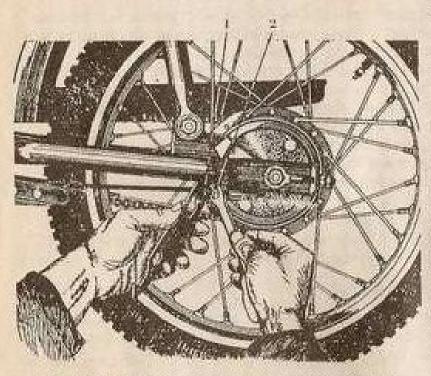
Регулировка тормоза заднего колеса: 1 – упор. 2 – гажка.
